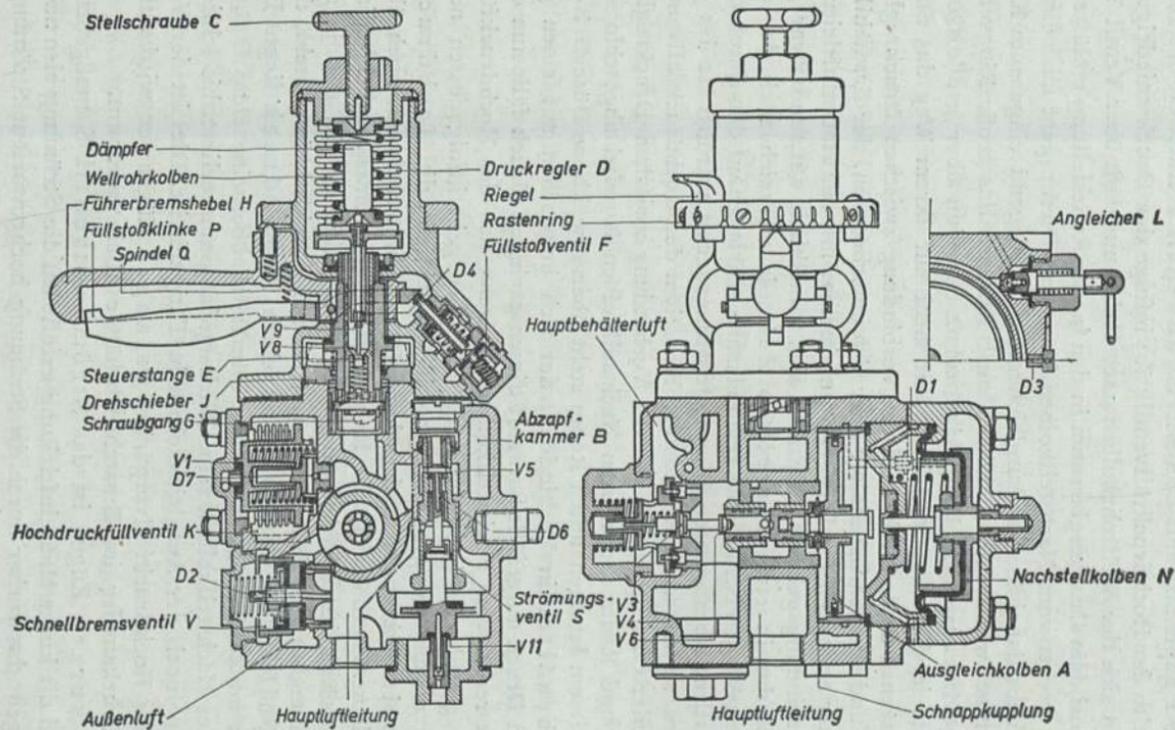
Das selbsttätige Führerbremsventil Bauart Knorr
